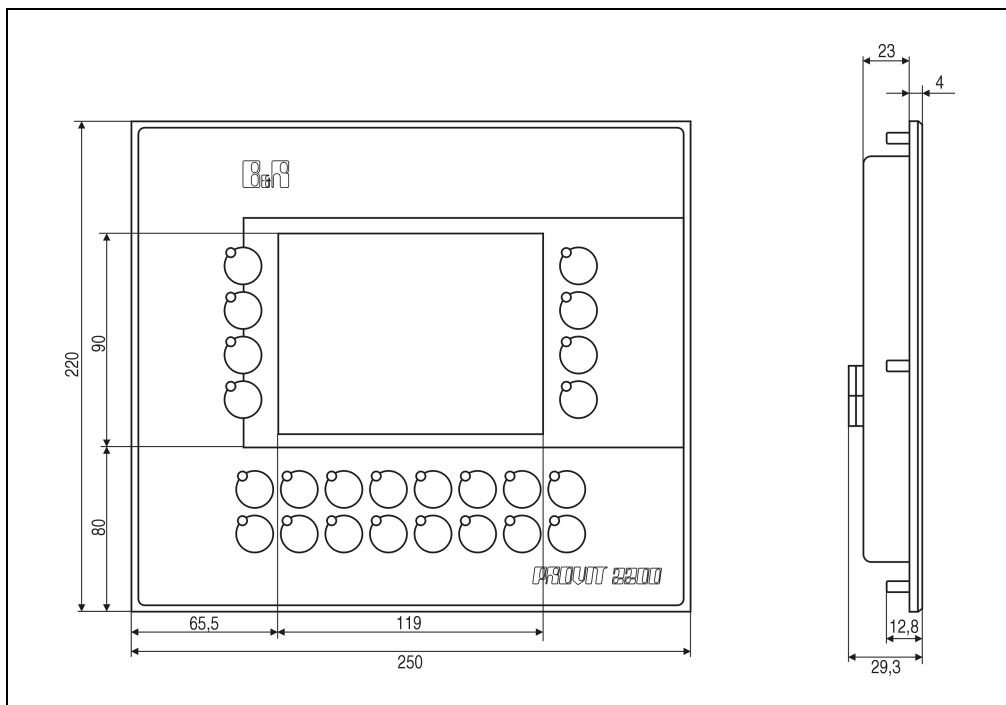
Dimensions des écrans 5D2219.01 et 5D2219.02
